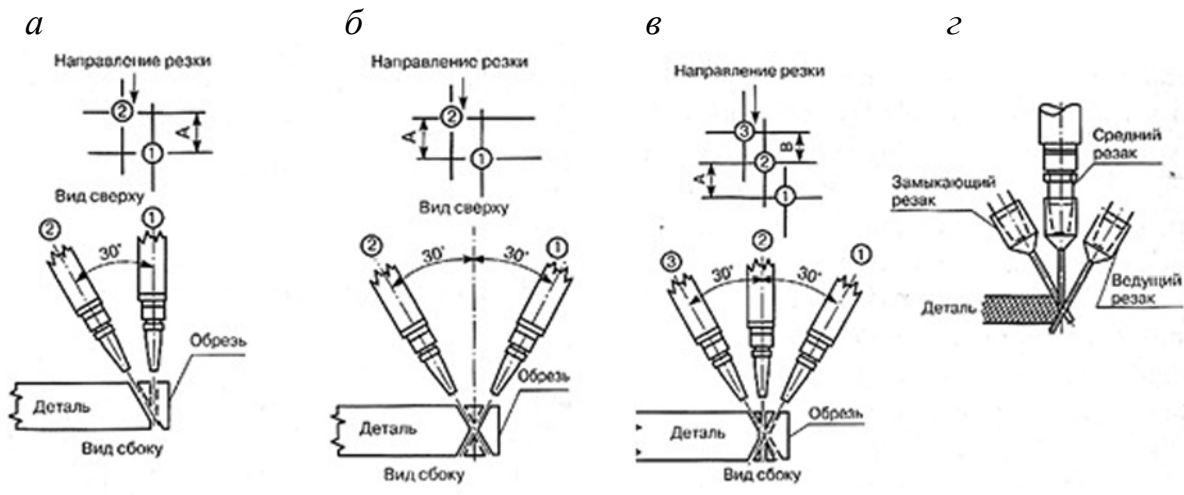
Схема выполнения разделки кромок под сварку:
